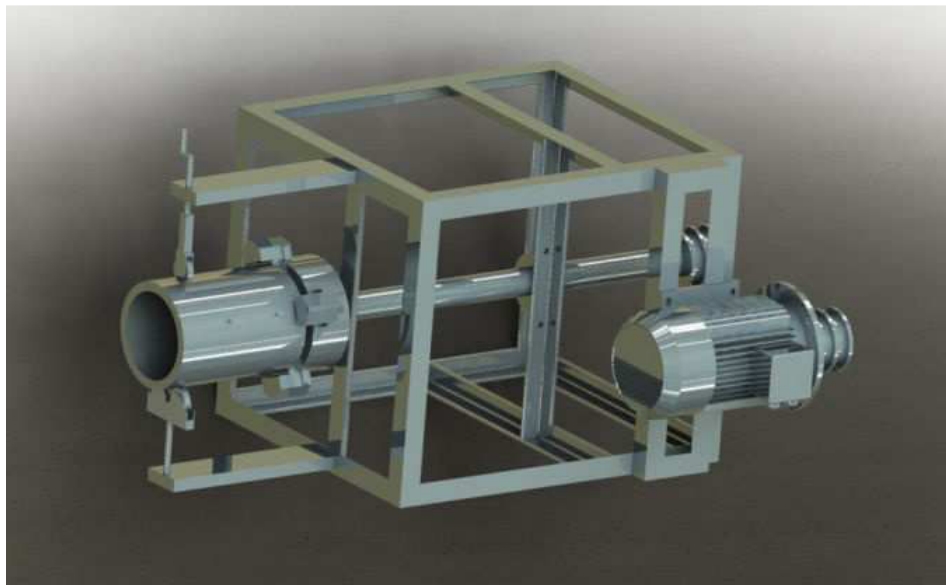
Mesin *Centrifugal Casting* Horizontal (www.custompartnet.com)
